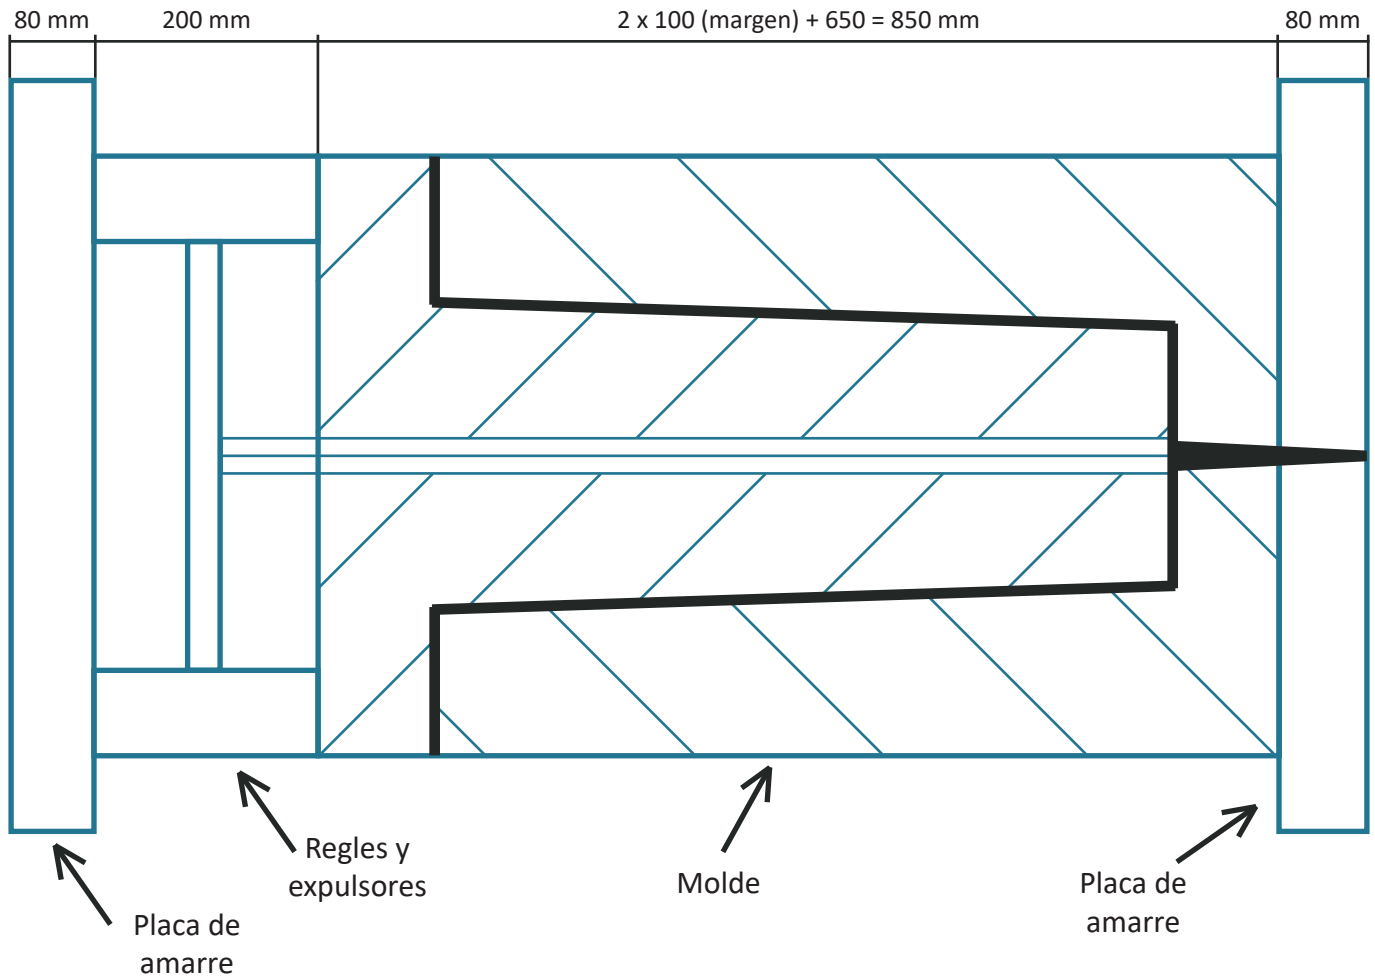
Molde del cuerpo que muestra el espesor mínimo de molde)
